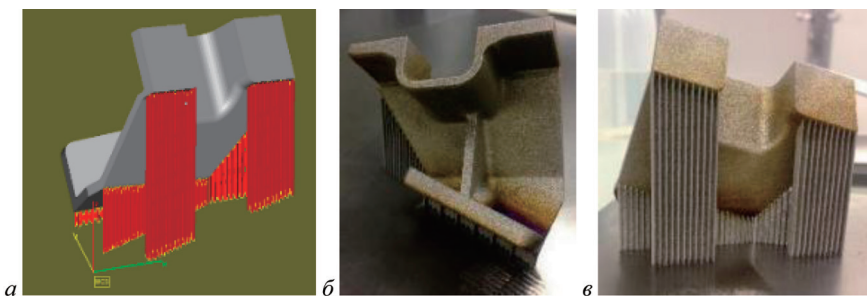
Расположение и конфигурация поддерживающих конструкций для изготавливаемой заготовки детали (а) и фотографии заготовки детали газотурбинного двигателя из сплава Ti6Al4V (б, в).
